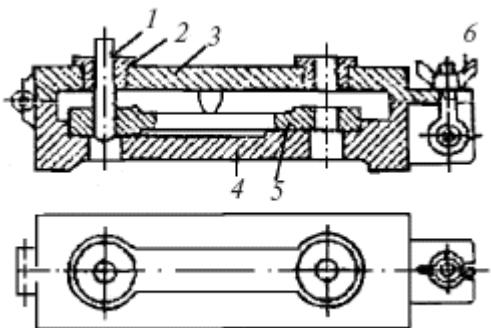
Приспособление с кондукторной плитой для сверления: 1 – сверло; 2 – втулка; 3 – кондукторная плита; 4 – нижняя часть кондуктора; 5 – обрабатываемая деталь; 6 – винт с гайкой-барашком
